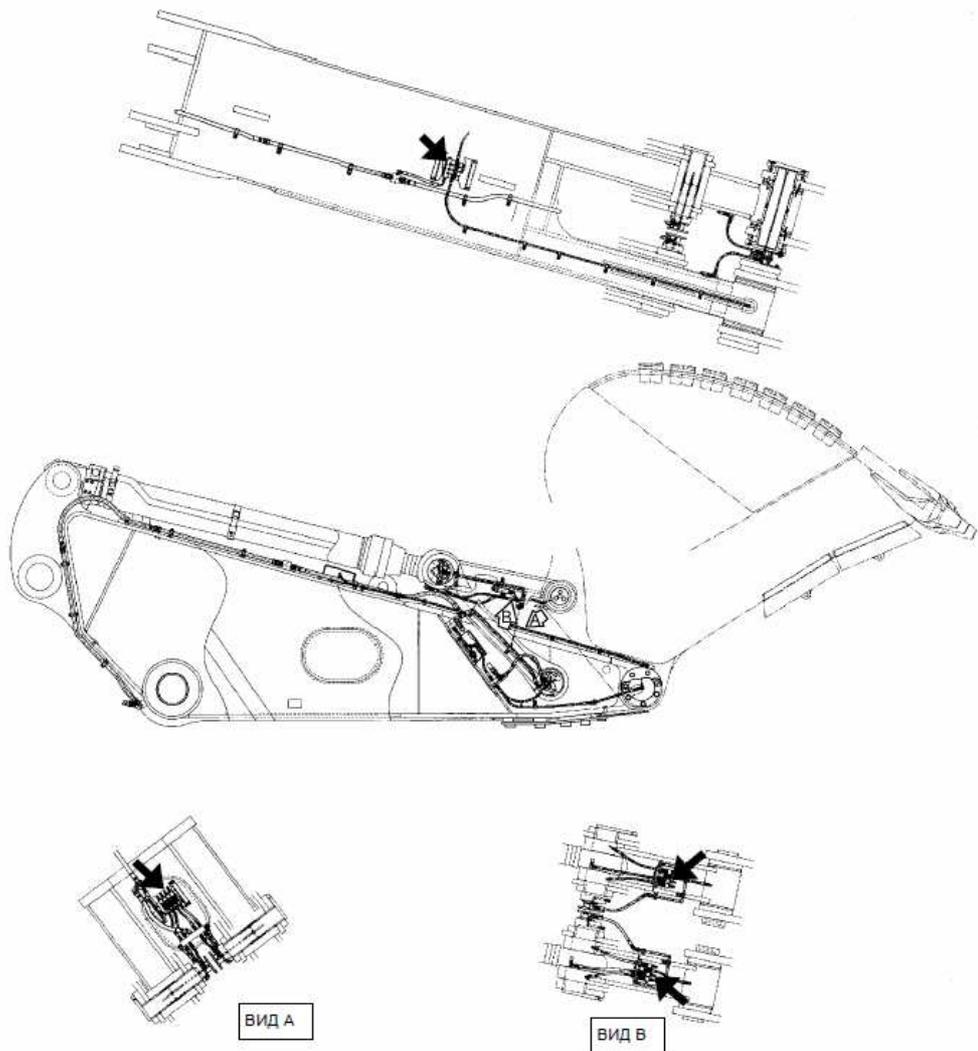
Смазка механизма открывания днища ковша
